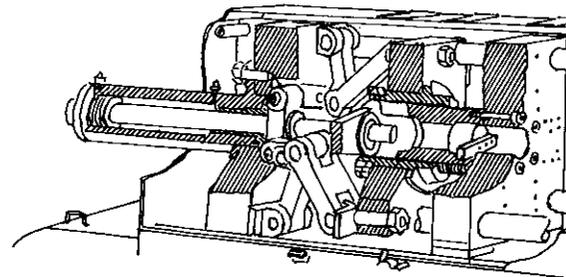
Versão simples de máquina de moldagem por injeção com fechamento do molde por um sistema de alavancas articuladas.
